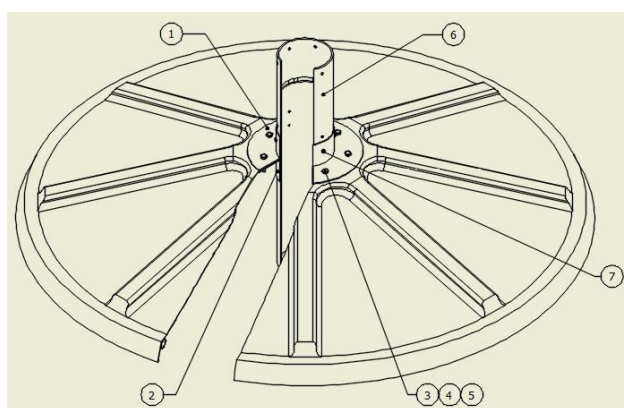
Aro tubular fixado na estrutura e corte da abertura.
